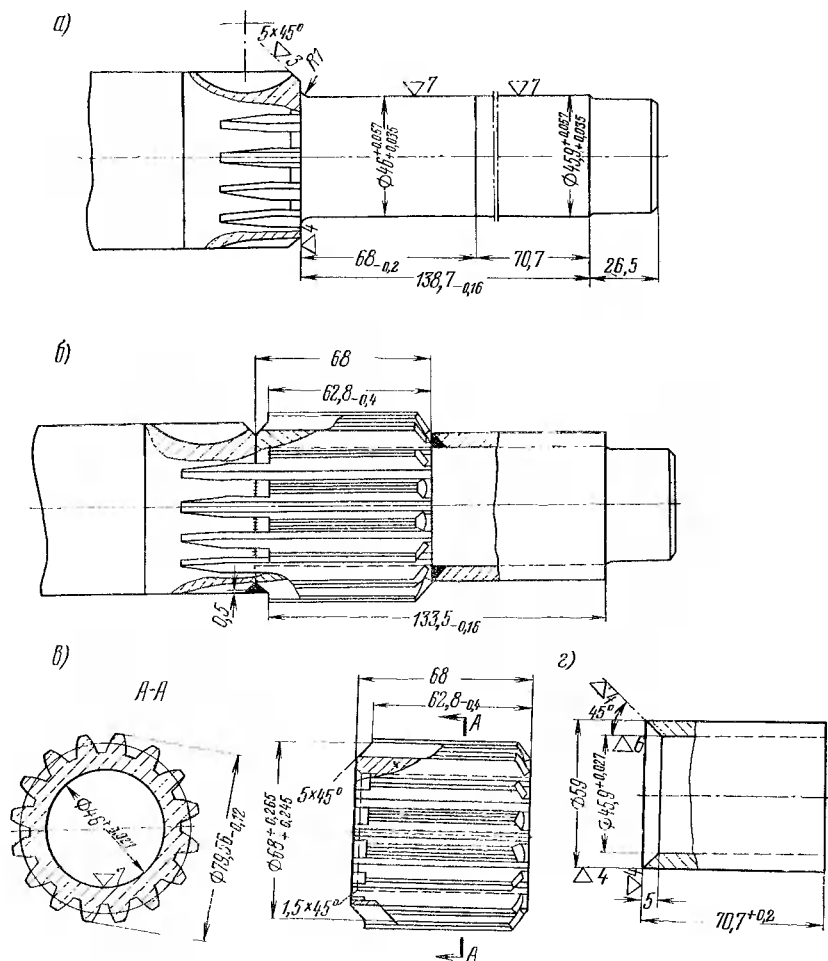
Ремонт промежуточного вала подстановкой ремонтного венца:
